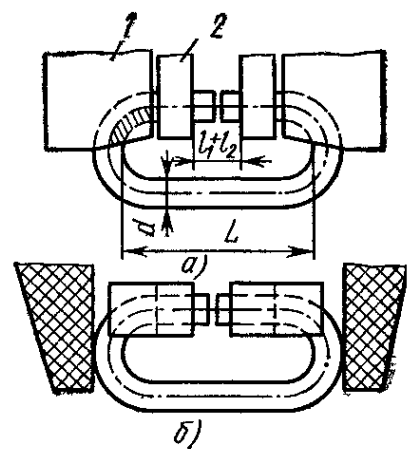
Схема зажимов при сварке звеньев цепей
